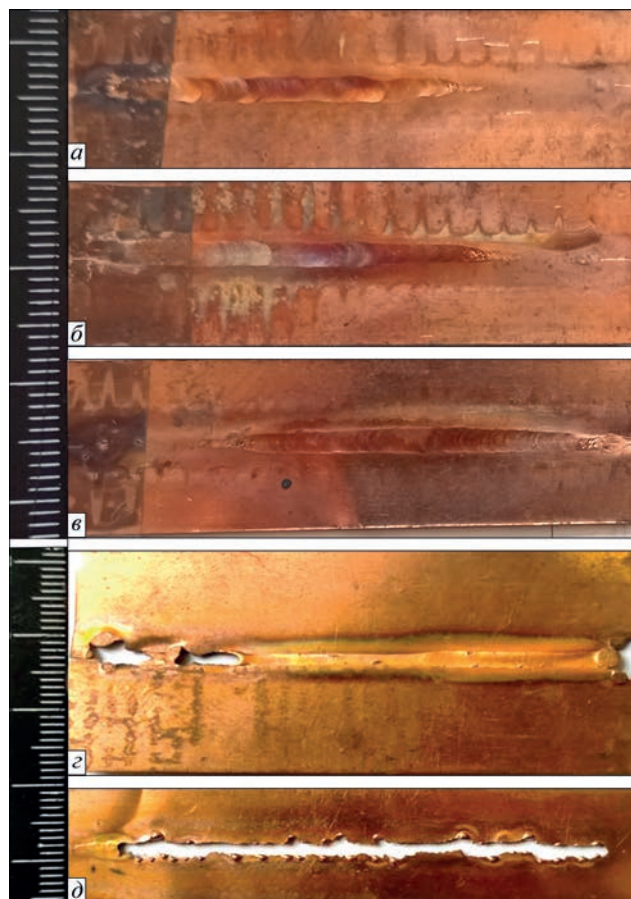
Зовнішній вигляд зварних швів виконаних по технологічній схемі зварювання II при $I_{зв}$, А: а – 20; б – 22; в – 24; г – 27; д – 30
